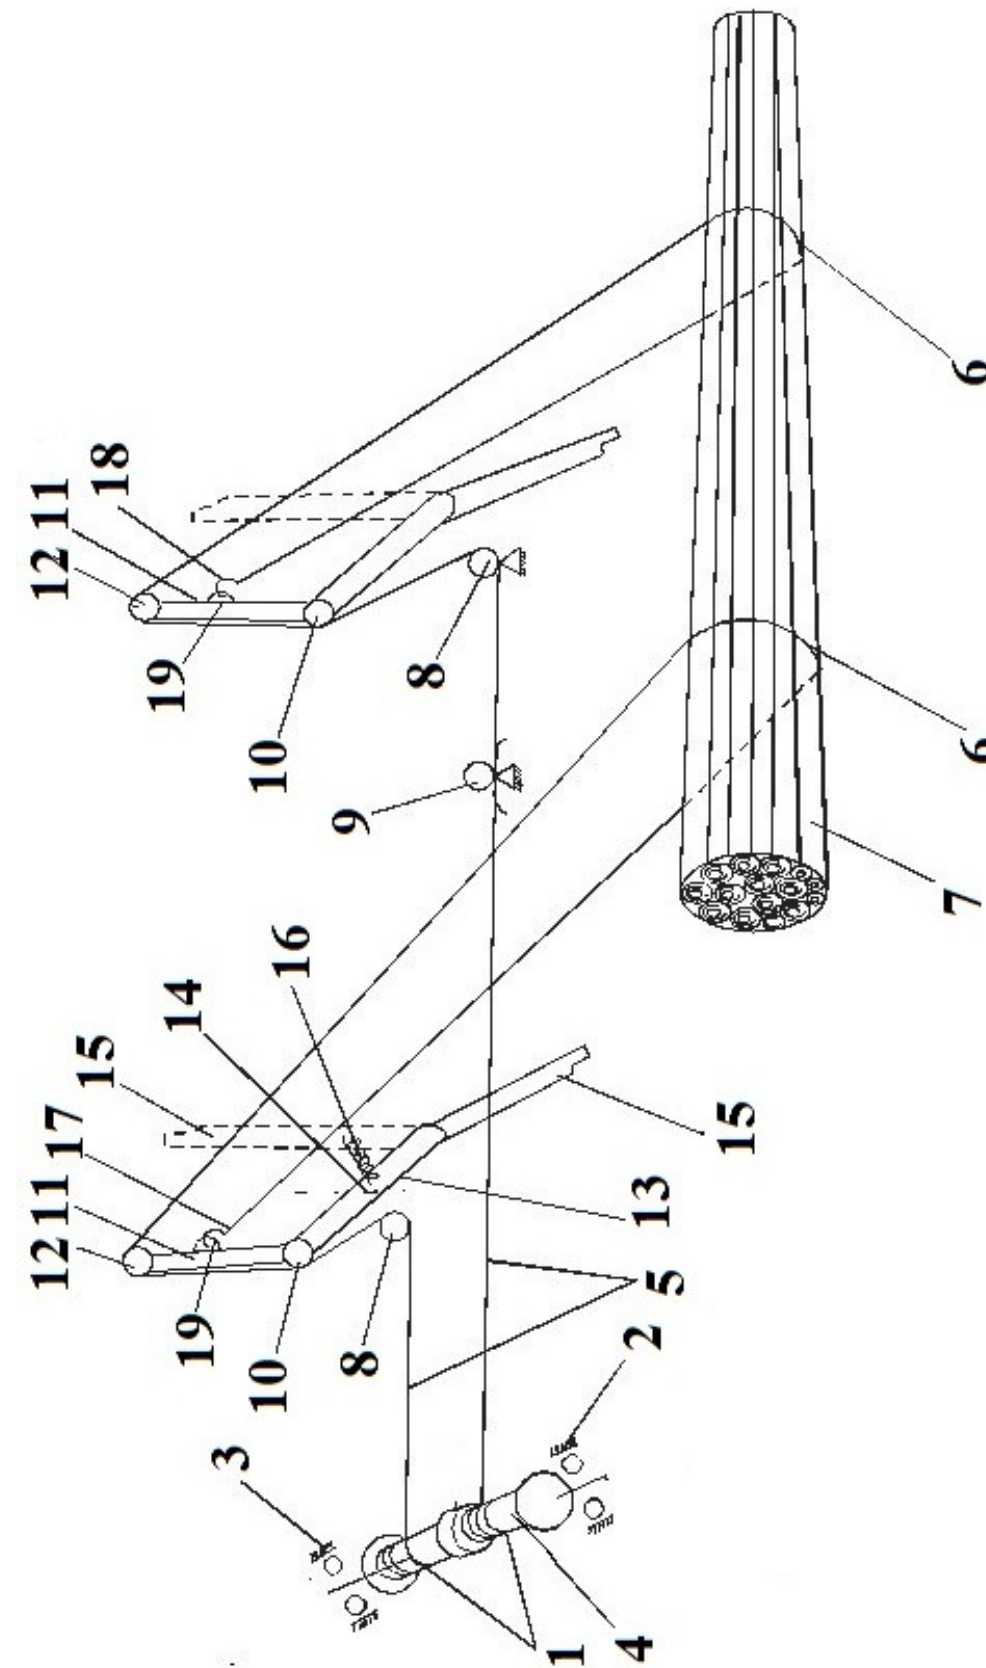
Компонуально-кінематична схема механізму навантаження: 1 – двобарабанна лобідка; 2, 3 – підшипникові опори; 4 – вал лобідки; 5 – вантажні троси; 6 – петлі; 7 – пакет деревинної сировини; 8, 10 – обвідні блоки; 9 – направляючий блок;
